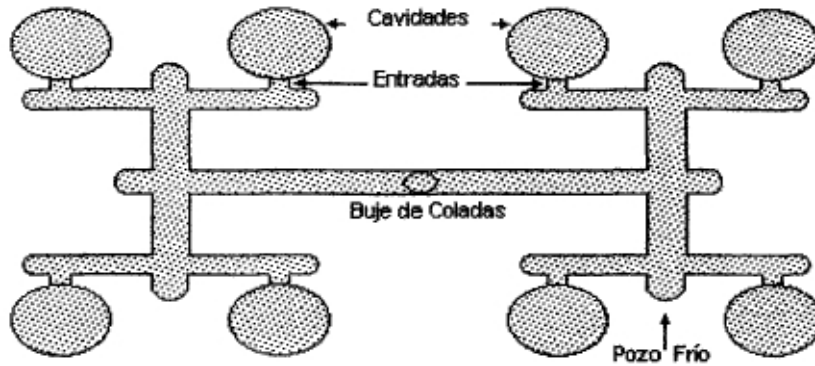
Esquema de un molde balanceado.<sup>5</sup>
